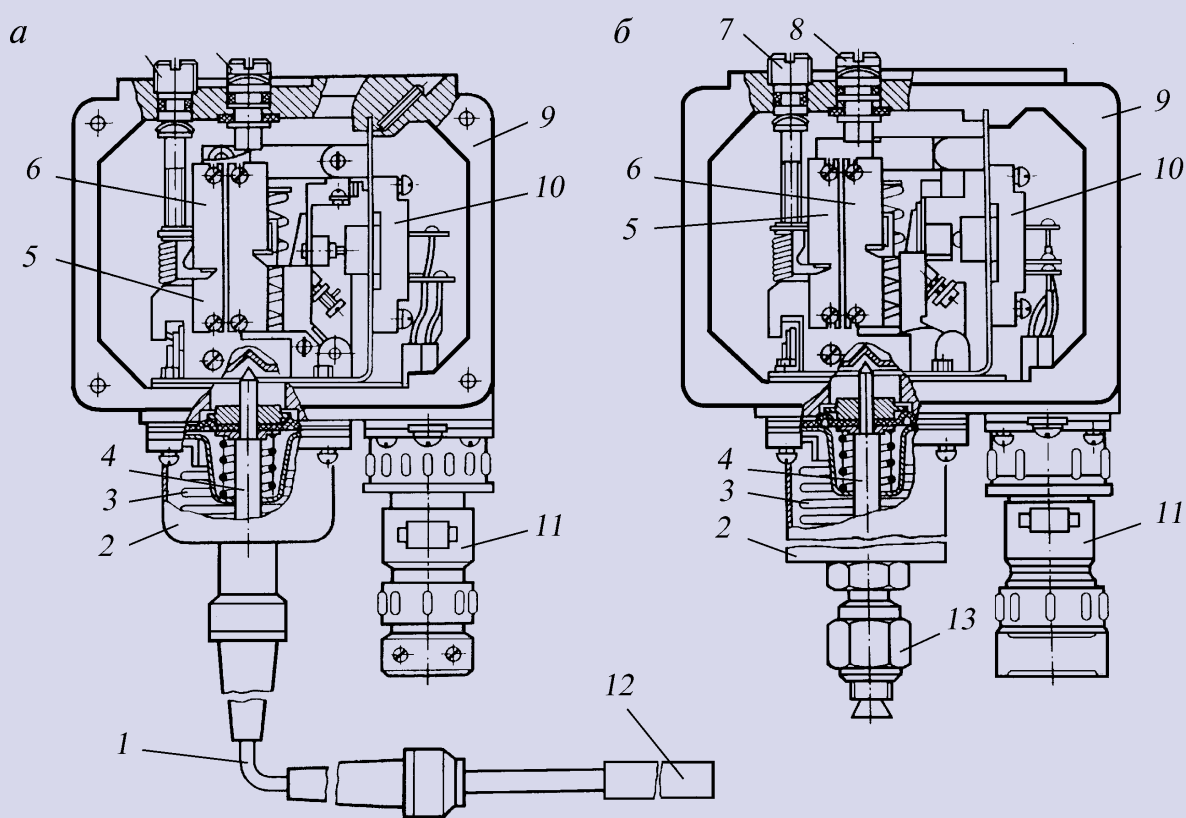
Реле температуры (а) и давления (б): 1 — капиллярная трубка; 2 — кожух сильфона; 3 — сильфон; 4 — шток; 5 — шкала настройки дифференциала; 6 — шкала настройки диапазона; 7 — винт настройки дифференциала; 8 — винт настройки диапазона; 9 — корпус; 10 — контактная система; 11 — соединительный штепсель; 12 — термобаллон; 13 — штуцер
